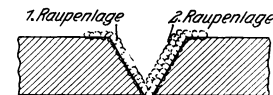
Ausfüllen einer Schweißfuge.
